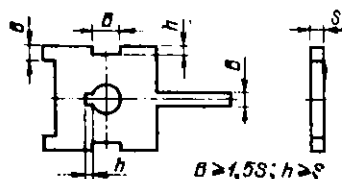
Минимальные размеры конструктивных элементов детали, получаемой выружкой
